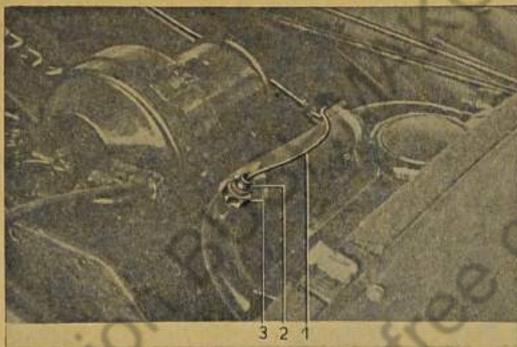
Fühler für Kühlwasser-Fernthermometer abschrauben
